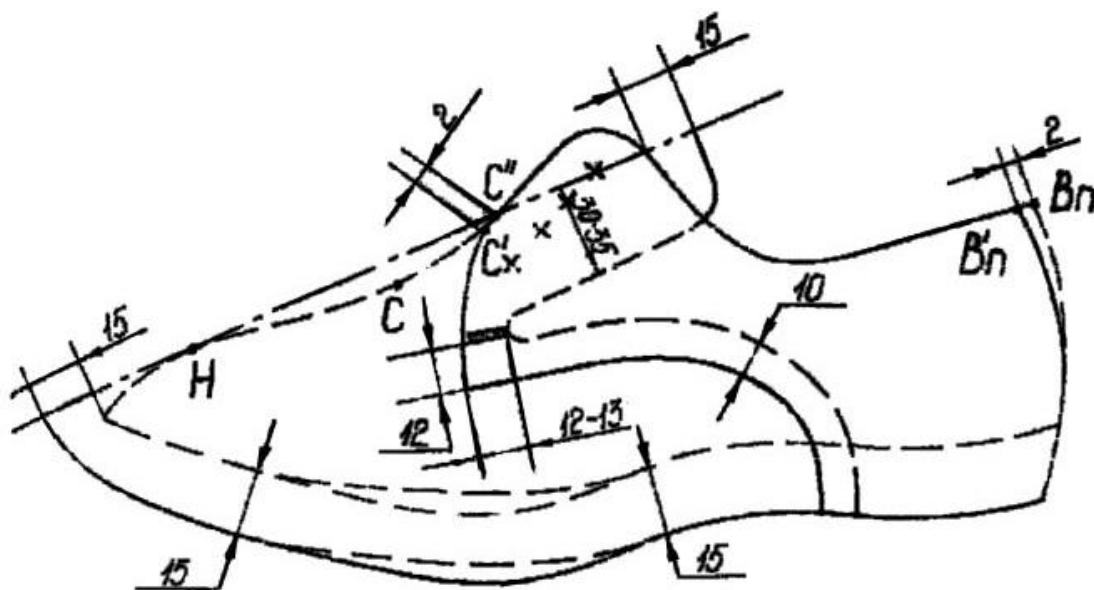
Побудова ґрунд-моделі макету заготовки
